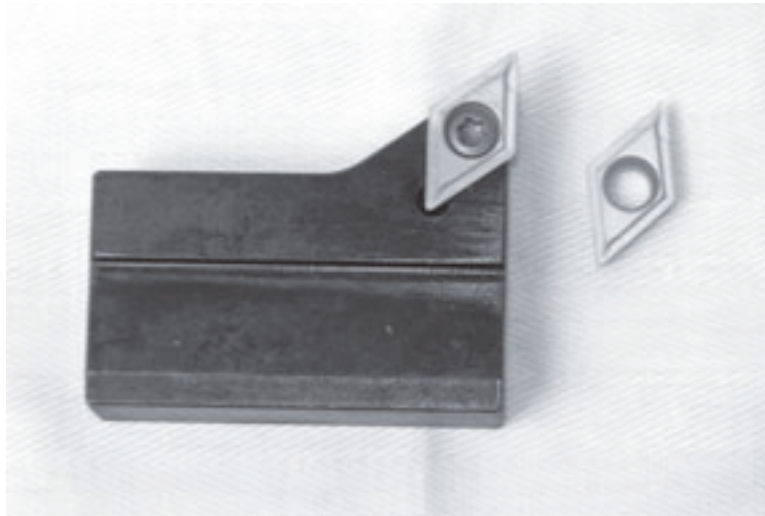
Der einschneidige Werkzeughalter mit Werkzeugeinsätzen wird zur Planbearbeitung von Flanschen verwendet.
